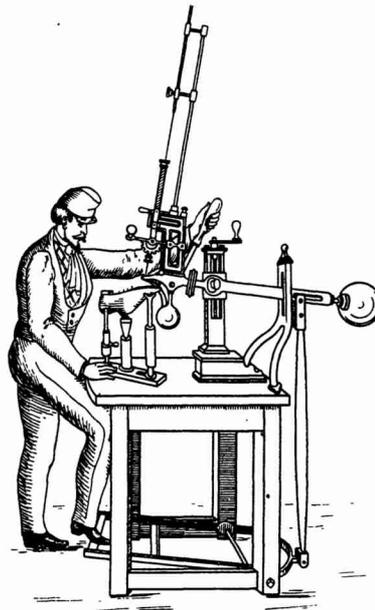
Sohlenschraubmaschine von Lemerrier (1854).
